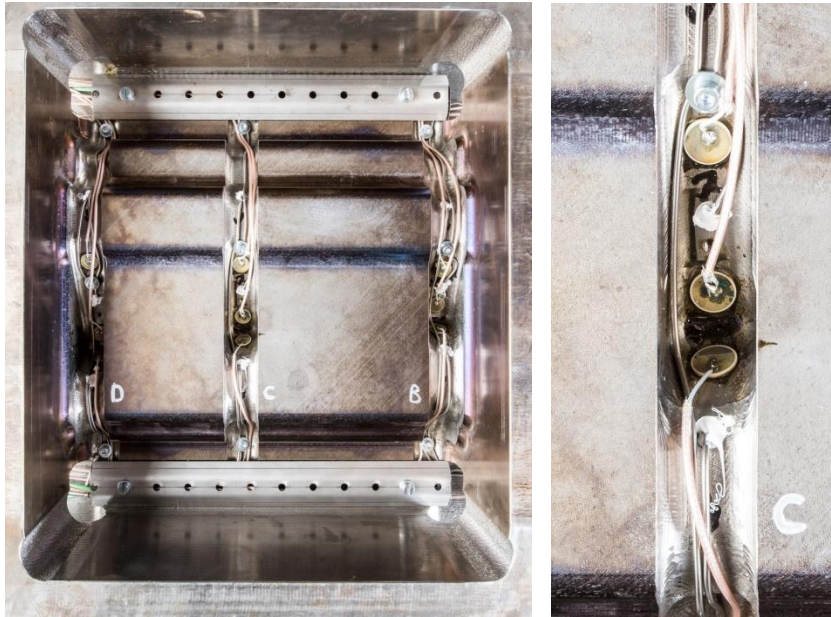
Integration der Ultraschallsensoren und deren Kabel in die vorgesehenen Taschen im closed-mold-Formwerkzeug (links Übersicht über drei „Schnitte“ à drei Sensoren und rechts Detail eines „Schnitts“)
